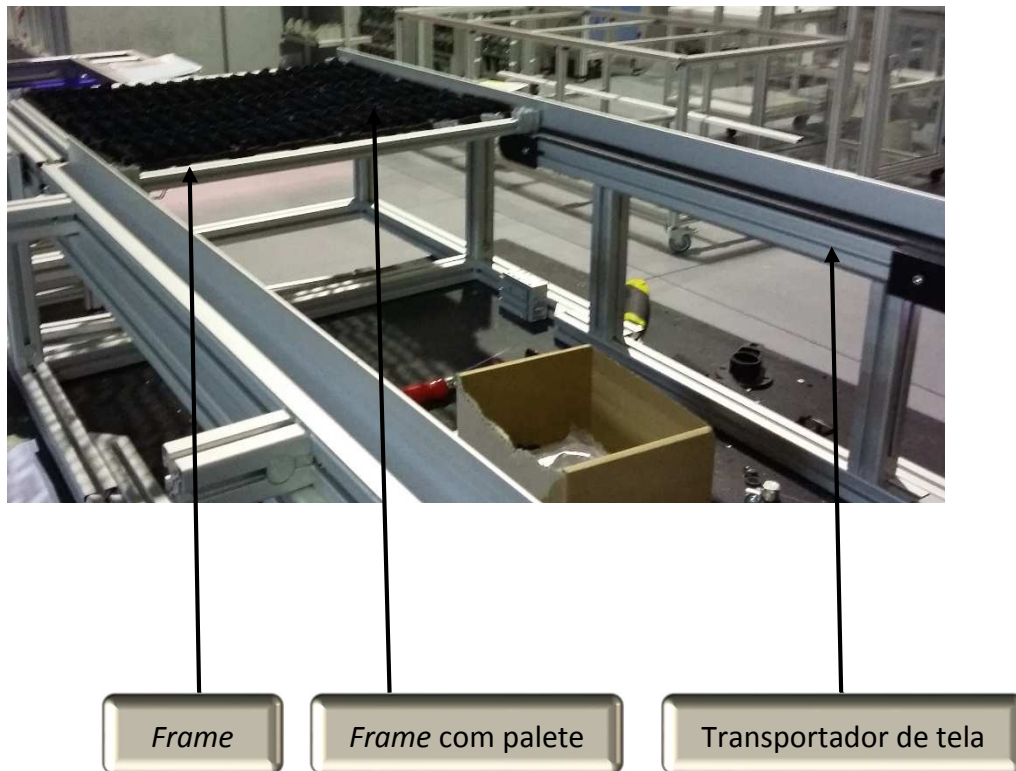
Teste do primeiro sistema de movimentação longitudinal
